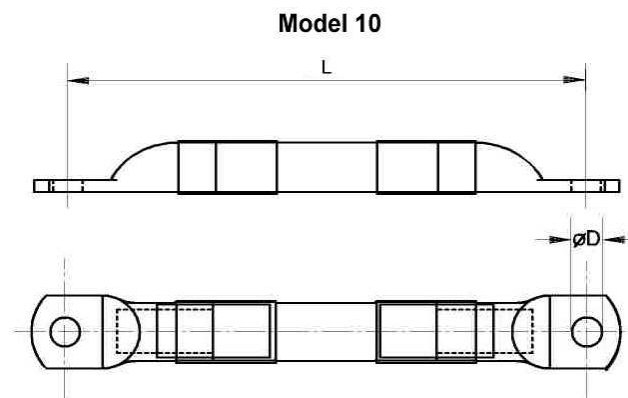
Kabelverbinder für M10 Innengewinde und Stehbolzen
